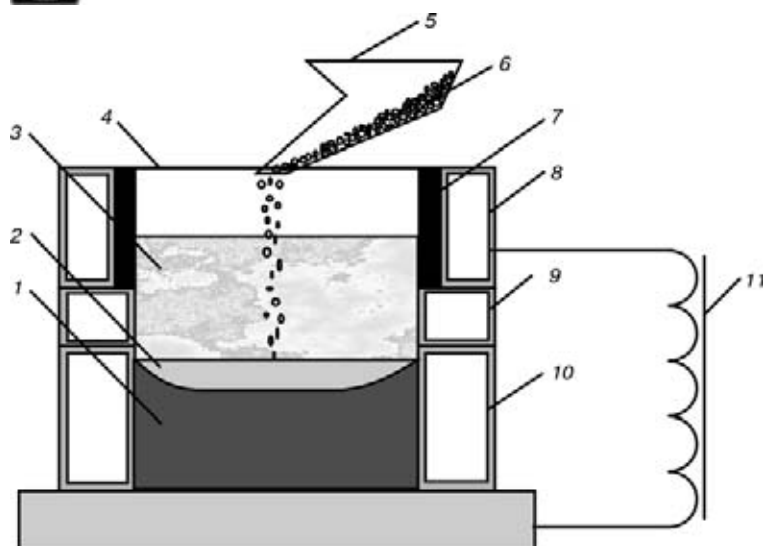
Схема выплавки слитка в токоподводящем кристаллизаторе [3]: 1 — слиток; 2 — металлическая ванна; 3 — шлаковая ванна; 4 — кристаллизатор; 5 — механизм подачи присадочного металла; 6 — кусковой присадочный материал; 7 — защитный слой (молибден, вольфрам и графит); 8–10 — секции кристаллизатора; 11 — трансформатор
